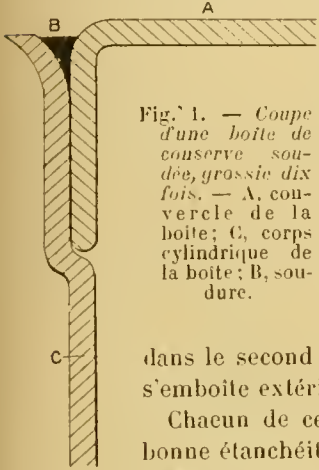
Coupe d'une boîte de conserve soudée, grossie dix fois. — A, couvercle de la boîte; C, corps cylindrique de la boîte; B, soudure.
